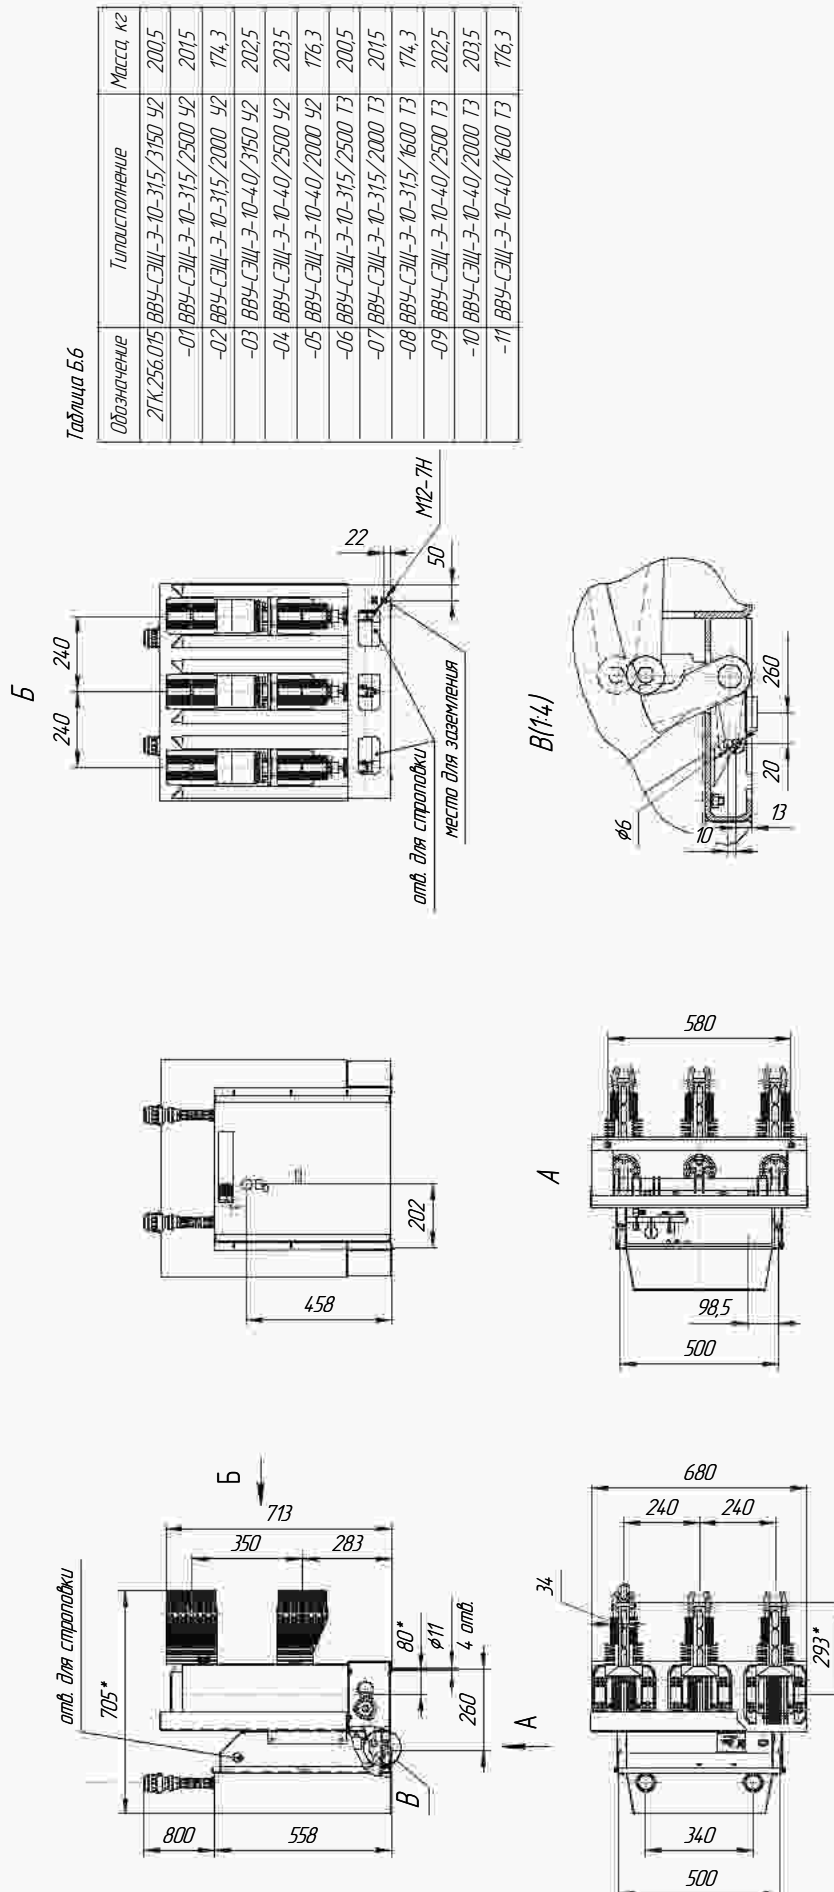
Габаритные, присоединительные и установочные размеры выключателя типа ВВУ-СЭЩ-Г-10-31,5(40)/3150(2000,2500)
